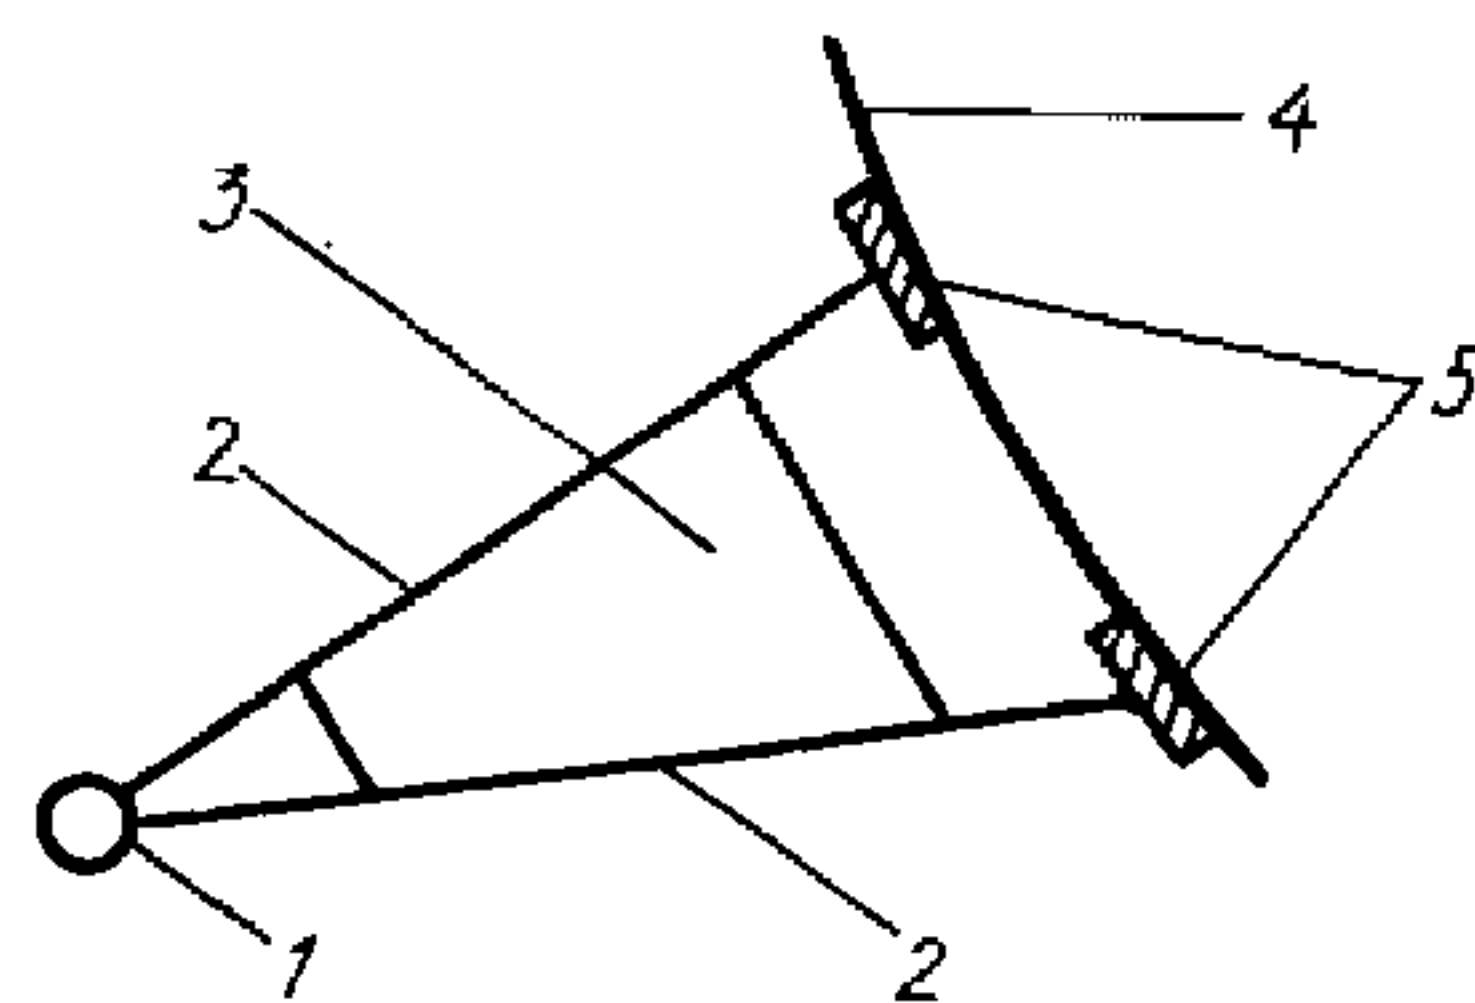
Полый скуловой киль с двойными листовыми элементами:
